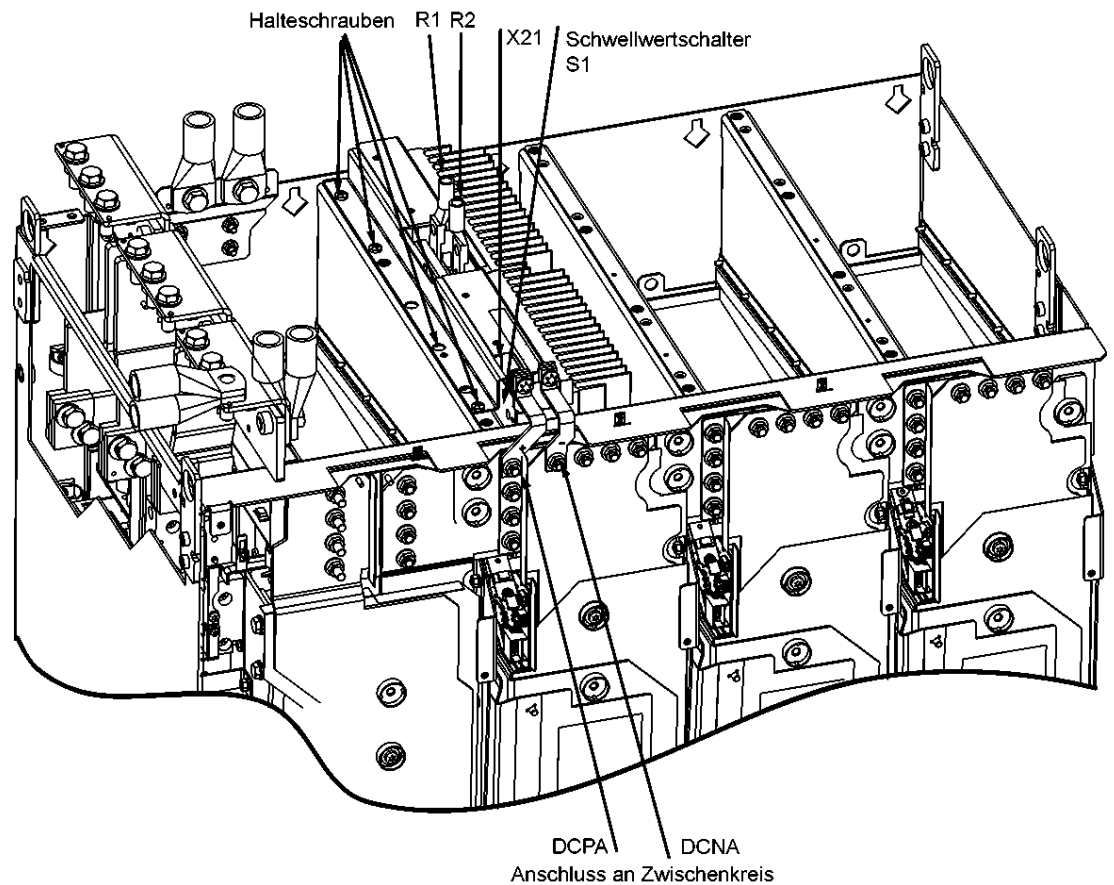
Montage eines Braking Module in Active Line Module bzw. Motor Module der Baugröße JX
